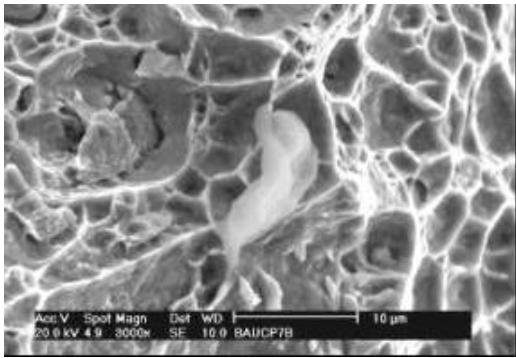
Fractografia por MEV da junta soldada com o consumível ER309L.
